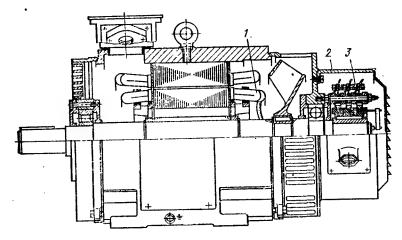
Аснихронный двигатель с фазным ротором 4AHK160. 1 — обмотка ротора; 2 — кожух; 3 — узел контактных колец.
